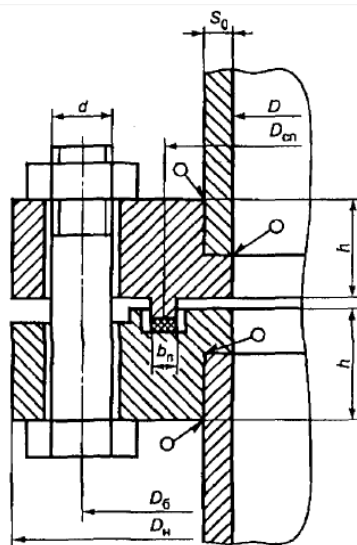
Фланцевые соединения с уплотнительной поверхностью типа шип-паз.
